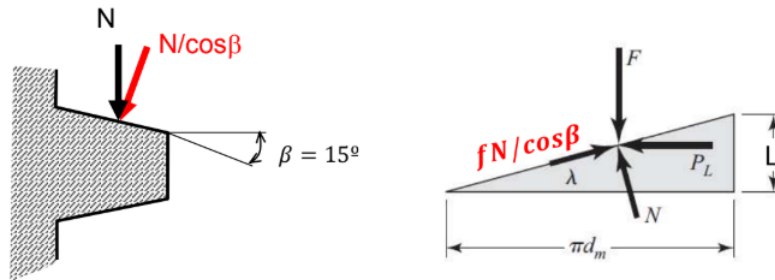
Rosca trapezoidal, dirección de las fuerzas al bajar la carga.
